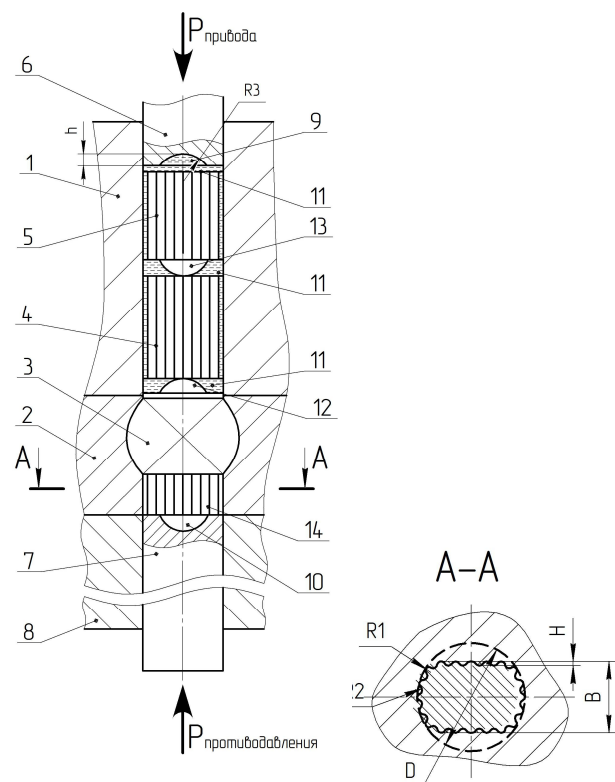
Схема устройства для реализации способа многоэтапного прессования заготовок пластической средой
